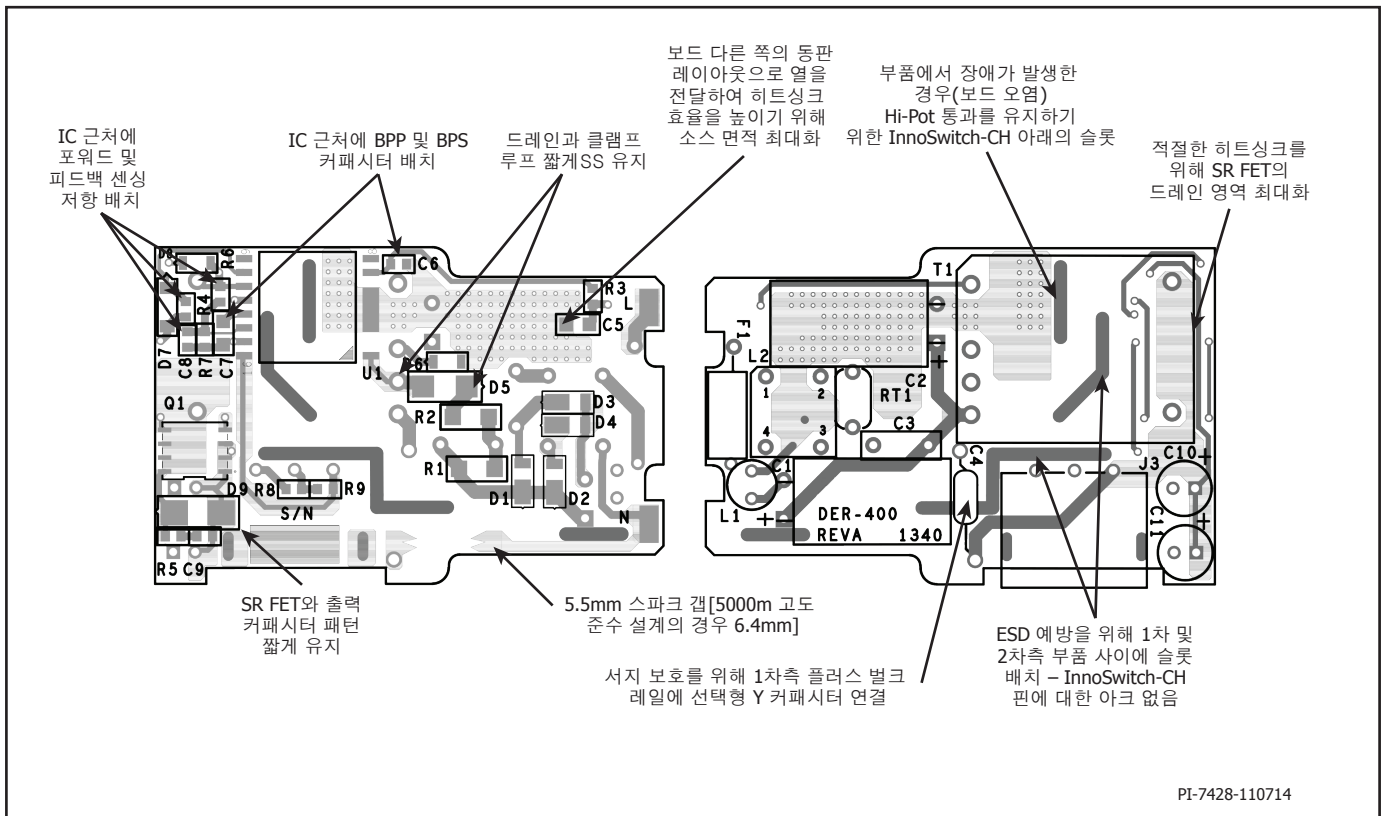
PCB 레이아웃 지침 하단(왼쪽), 상단(오른쪽)
